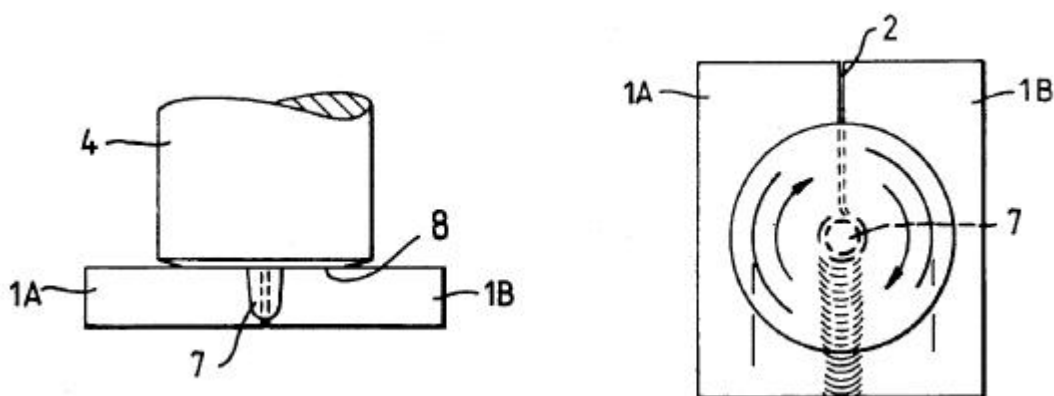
Vista frontal e de topo do processo de solda por fricção e mistura
